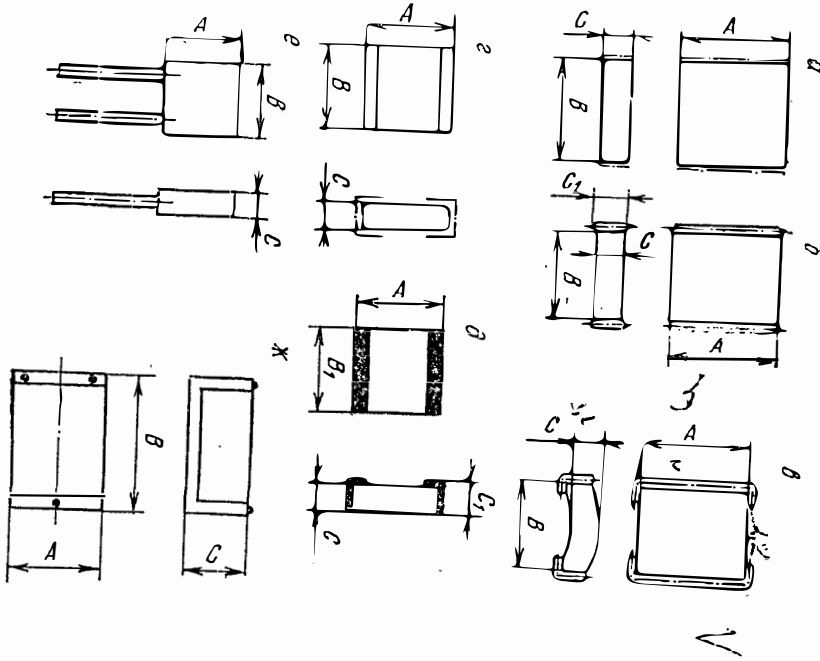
Габаритные чертежи миниатюрных конденсаторов, типов:
